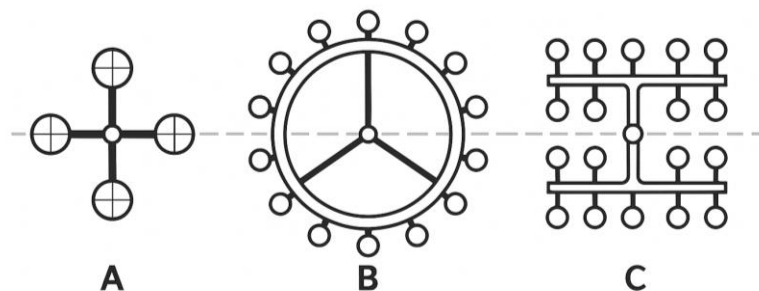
konstrukční řešení vtokové soustavy [15]
